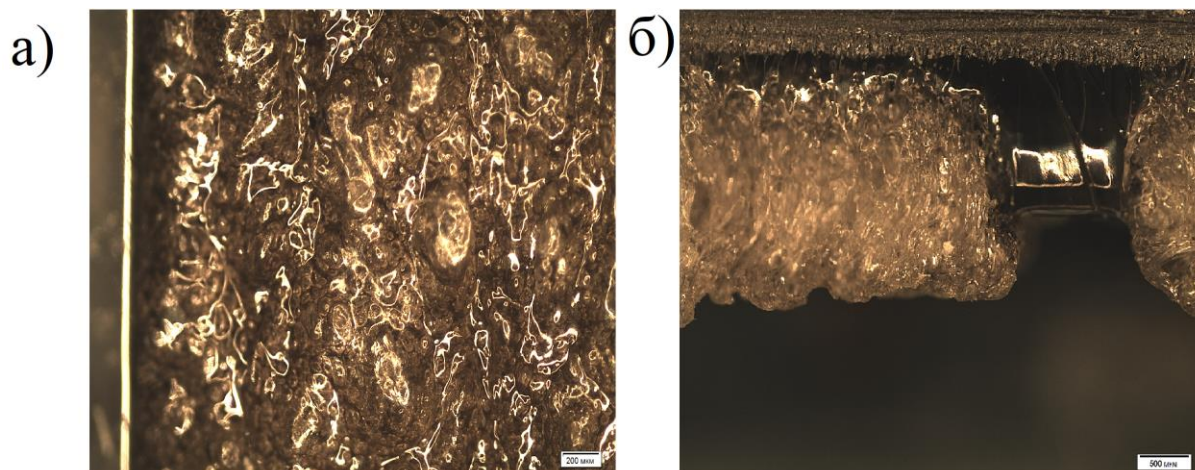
Валик на пластинке толщиной 2мм: а) вид сверху, увеличение x50; б) вид разлома
